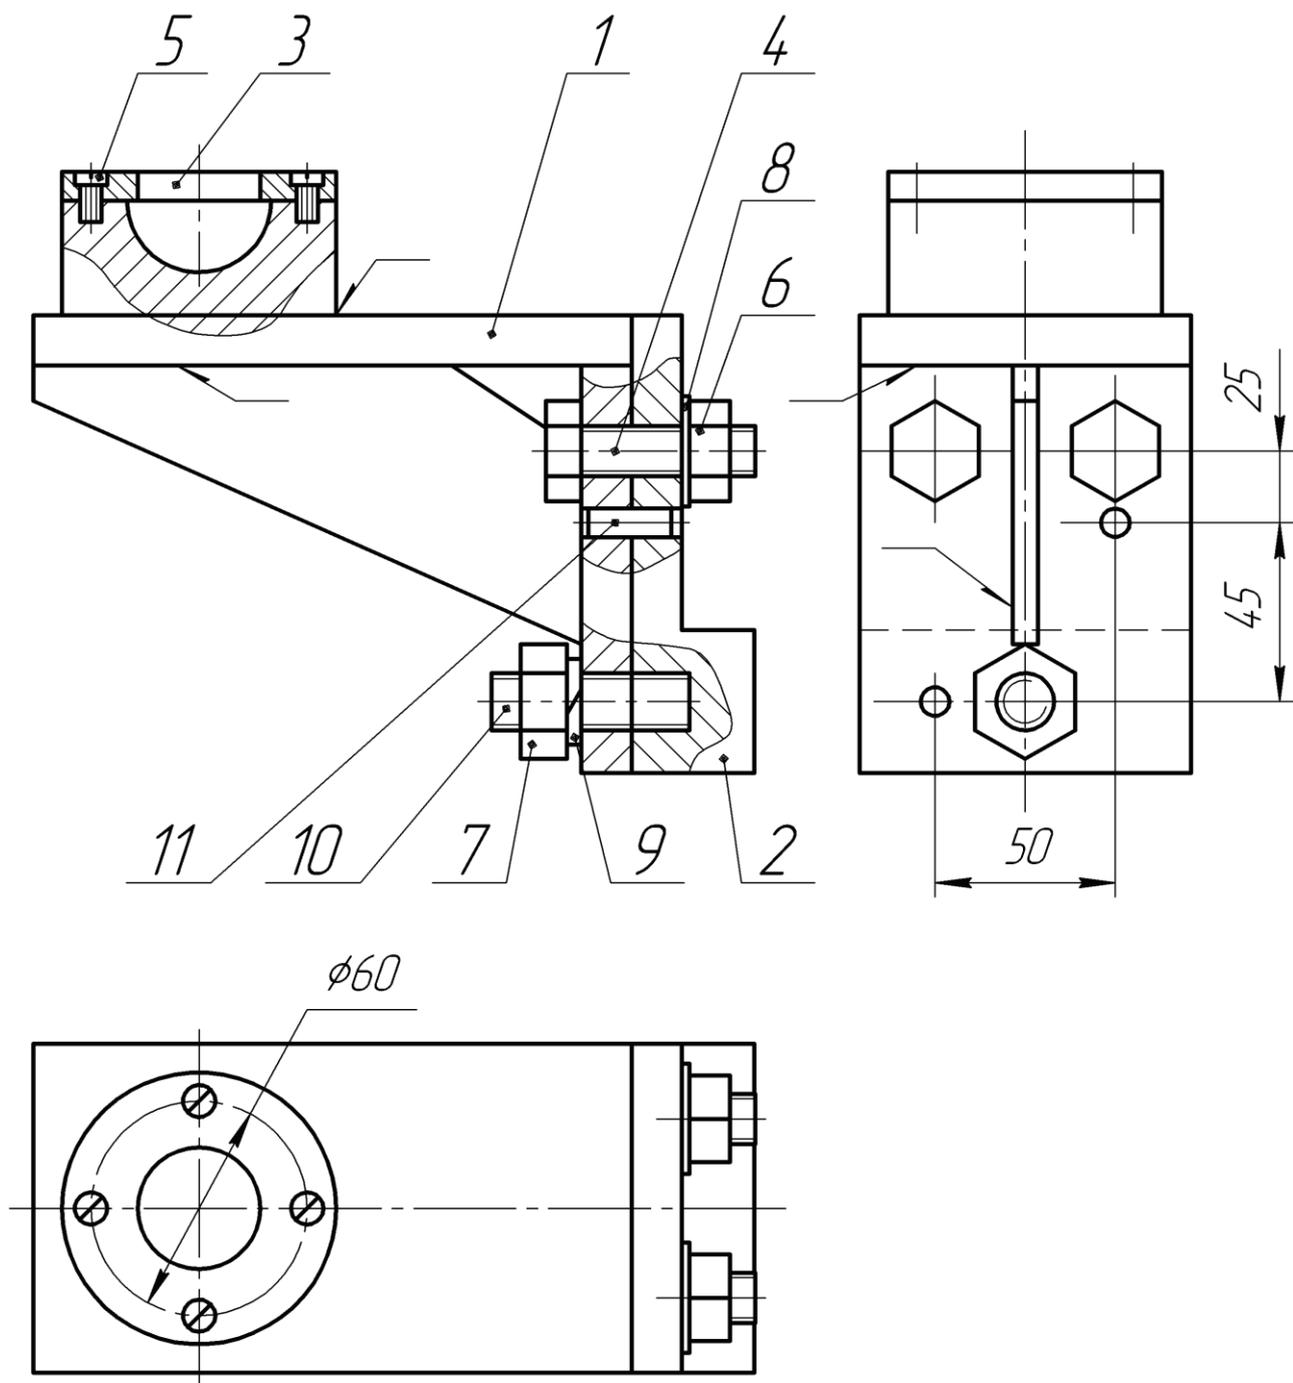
Сборочный чертеж изделия «Кронштейн»
